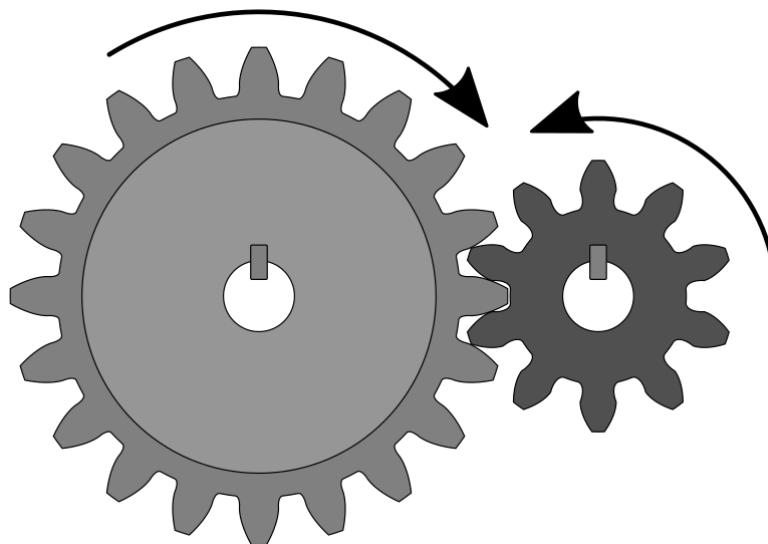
Engranaje de corona y piñón con flechas de sentido de giro.
